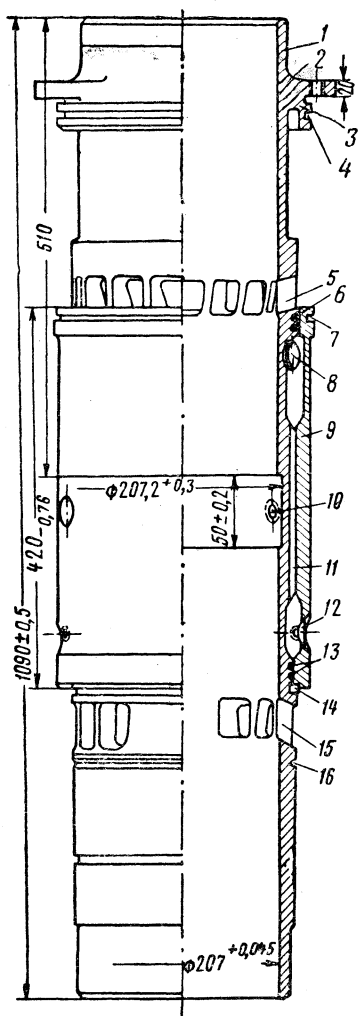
Разрез цилиндрической гильзы дизеля 2Д100:
